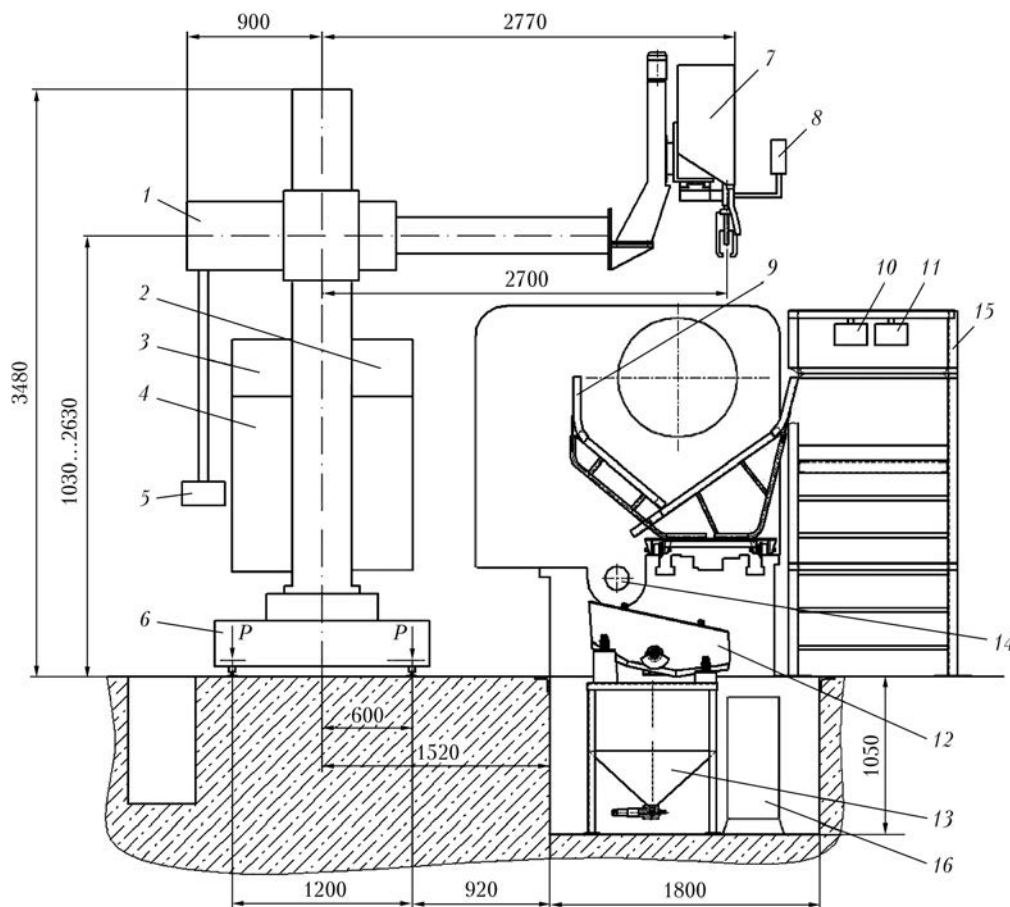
Схема модернизированной установки для наплавки прокатных валков заготовительных станков: 1–16 — см. в тексте
